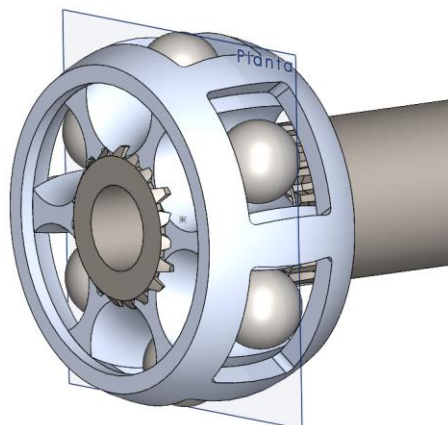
Elementos junta fija ensamblado respecto al plano planta del núcleo. Elaboración propia.
